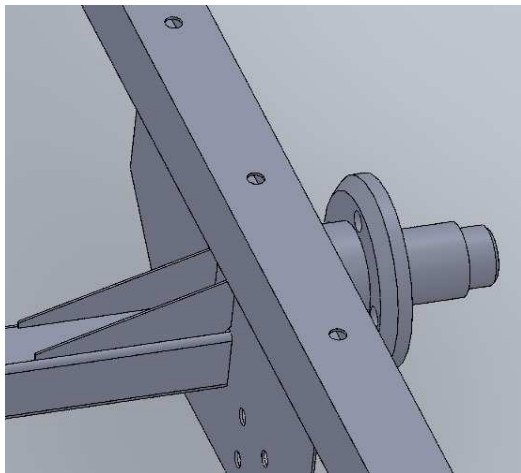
Konstrukční návrh přívěsu – varianta 2. Detailní pohled na spojení tažného kloubu s přírubou a čtvercových profilů. Zřetelně jsou vidět otvory pro šrouby. Otvory jsou průchozí celým profilem.
